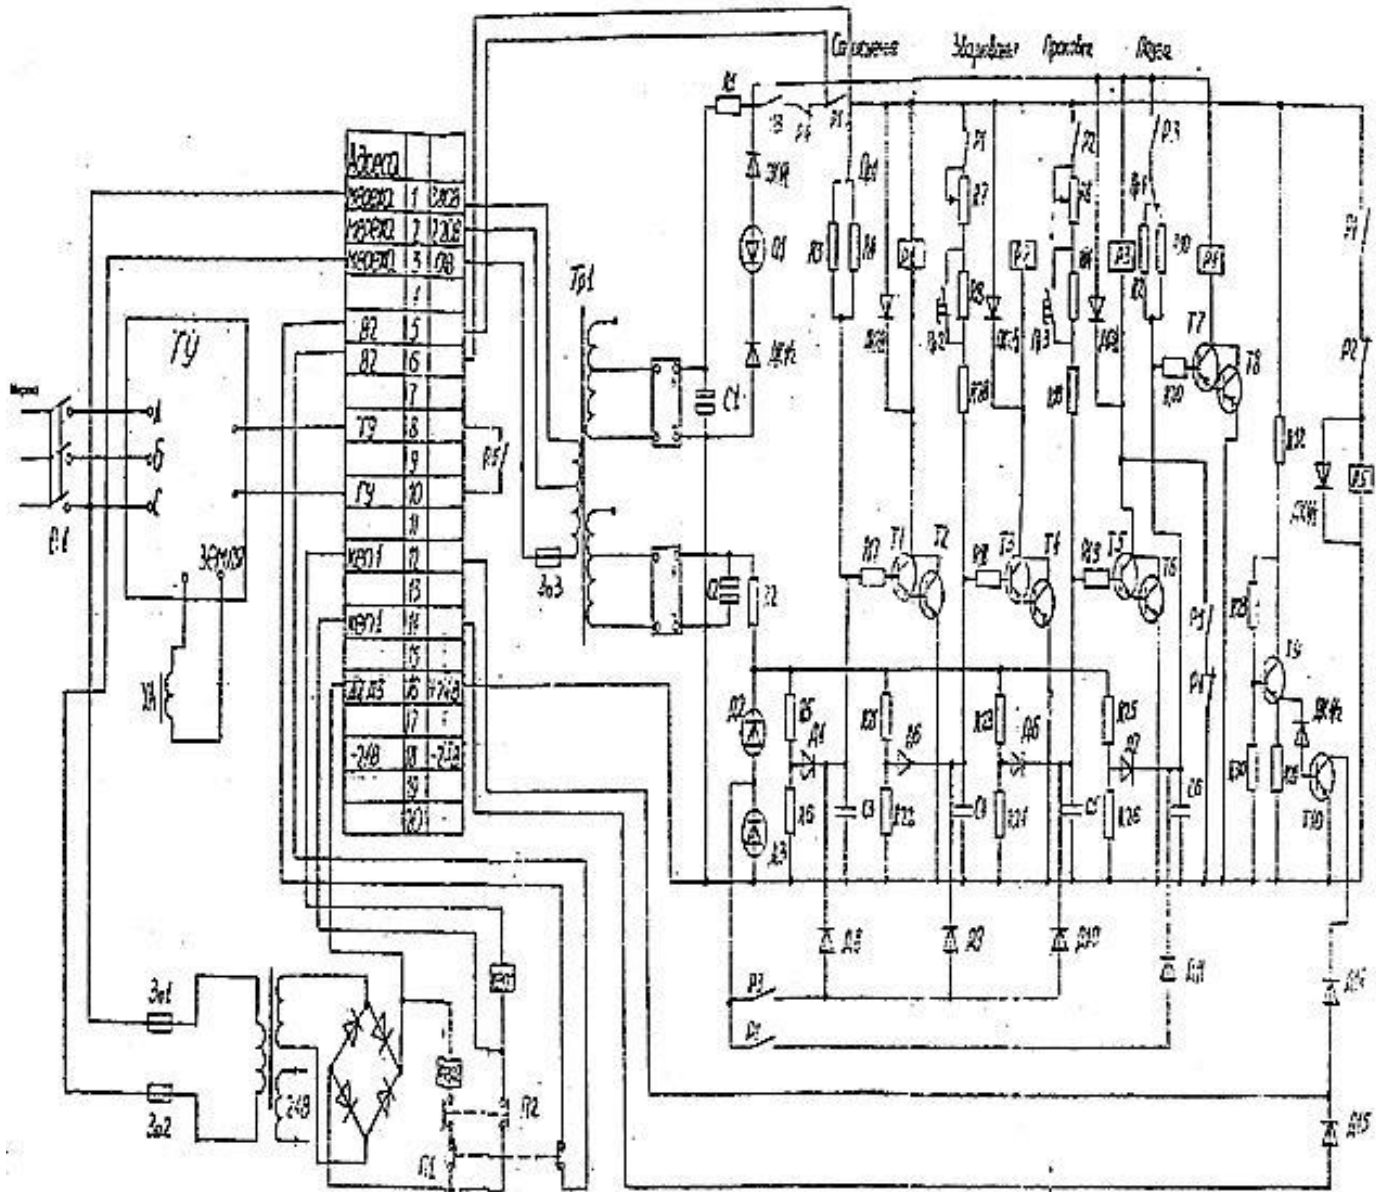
Принципова електрична схема машини для ультразвукового зварювання типу МТУ-0,4
